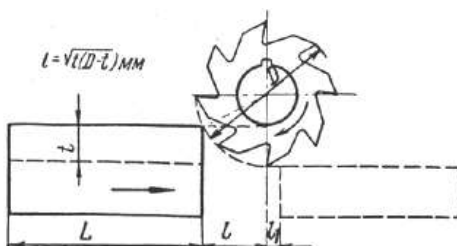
Врезание и перебег цилиндрической фрезы
